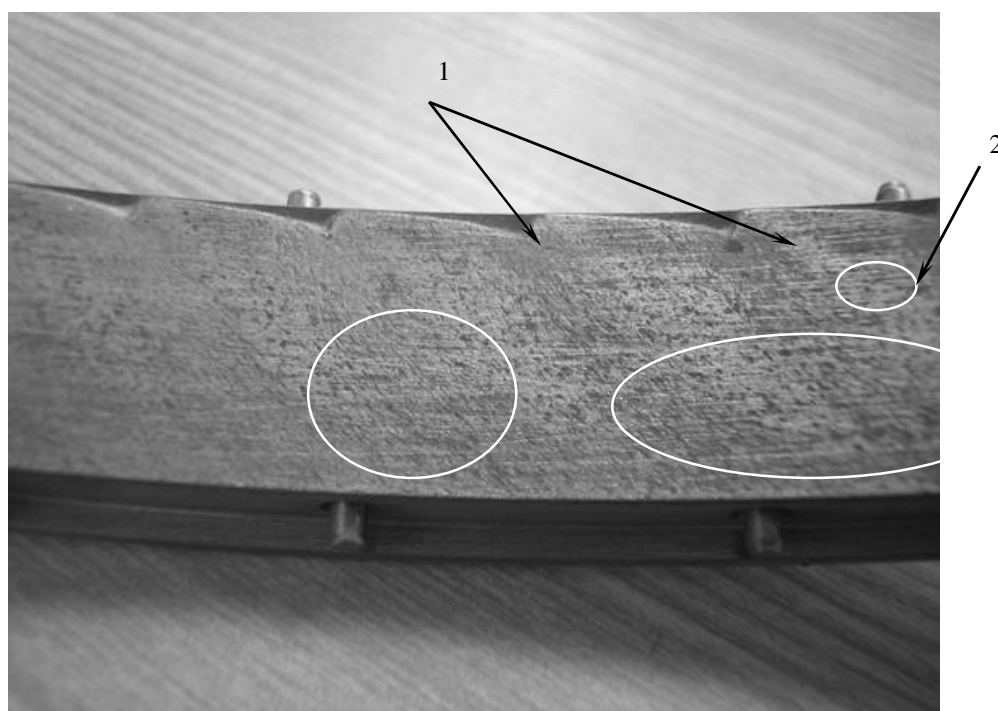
Кольцо рабочего колеса компрессора вертолетного двигателя. Дефекты: 1 – сколы; 2 – пористость
